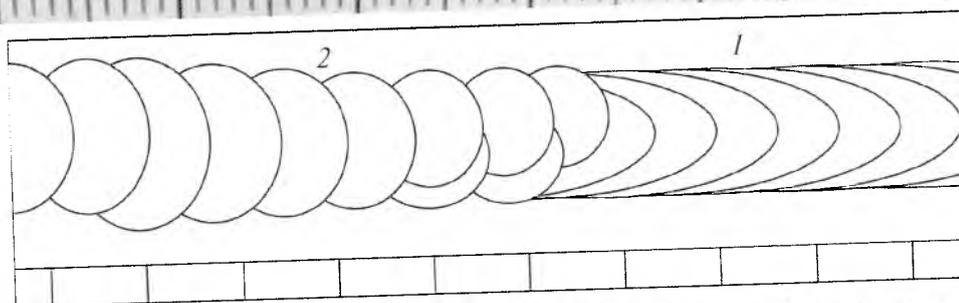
Стыковое сварное соединение обечайки сосуда. Правый участок 1 шва выполнен автоматической сваркой. Левый участок 2 – ремонтный, выполнен ручной дуговой сваркой в среде защитных газов.
